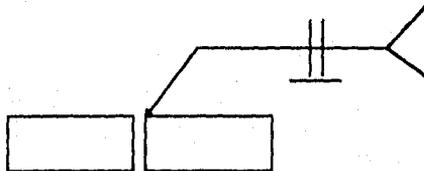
Efectuar la soldadura en placas colocadas a tope, sin preparación, suelde por ambos lados, la soldadura del lado de arriba debe quedar a ras.
